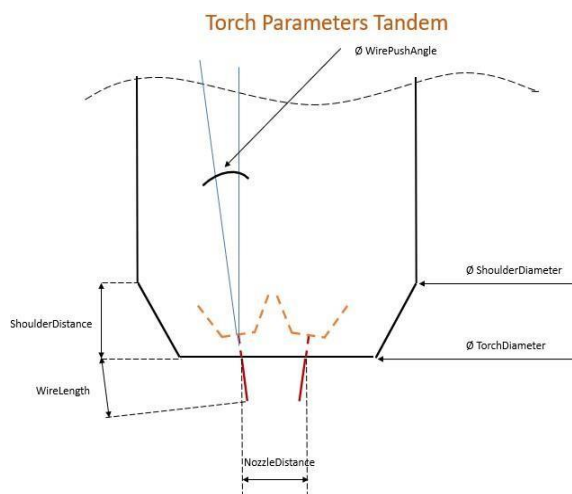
Tandem dimensions: размеры сопла тандемной горелки
